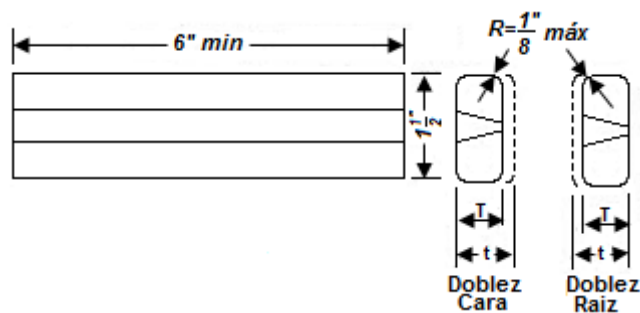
Especímenes placas soldadas de lado según ASTM E190
